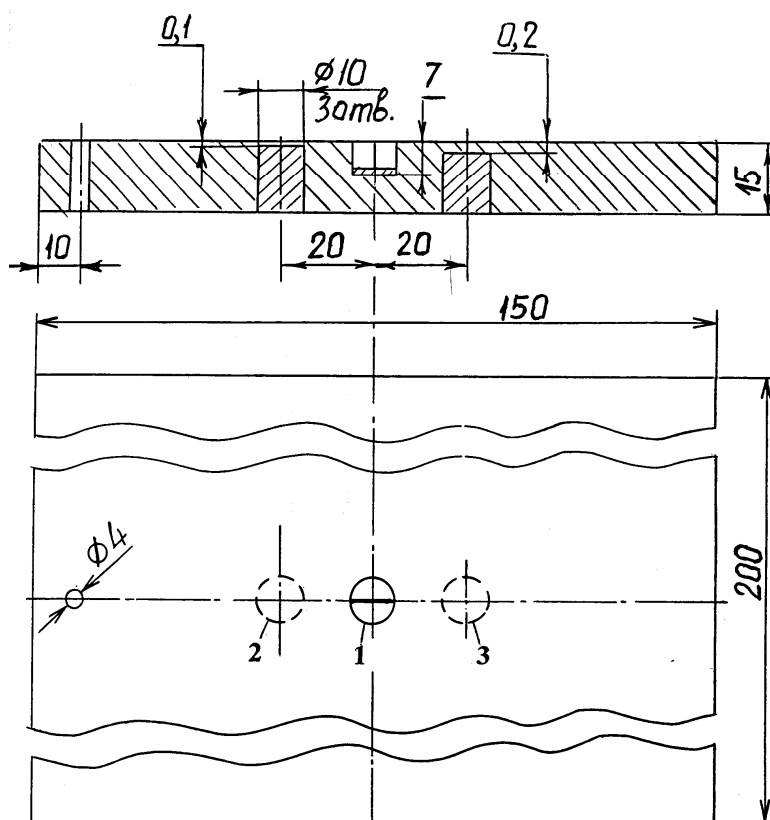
Контрольный образец МО-1 Шелихова Г.С.
